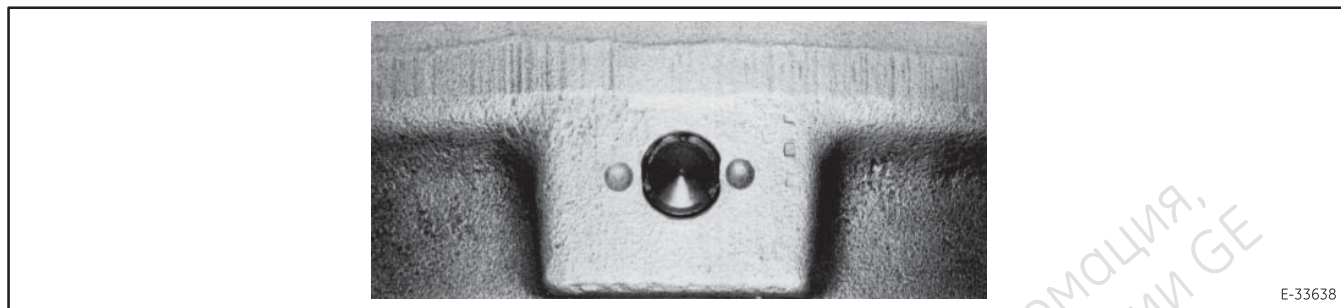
Сапун в упорном кольце подшипника типа "AP".
